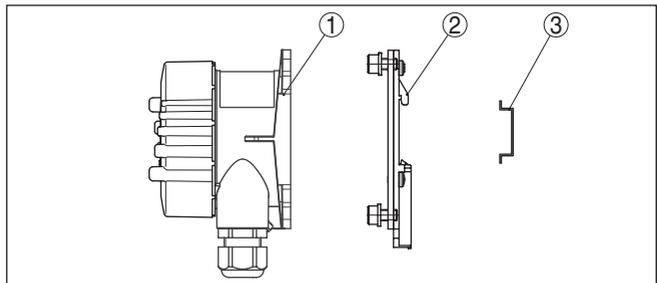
VEGABOX 03 con carcasa de aluminio y acero inoxidable para el montaje en regleta de montaje
